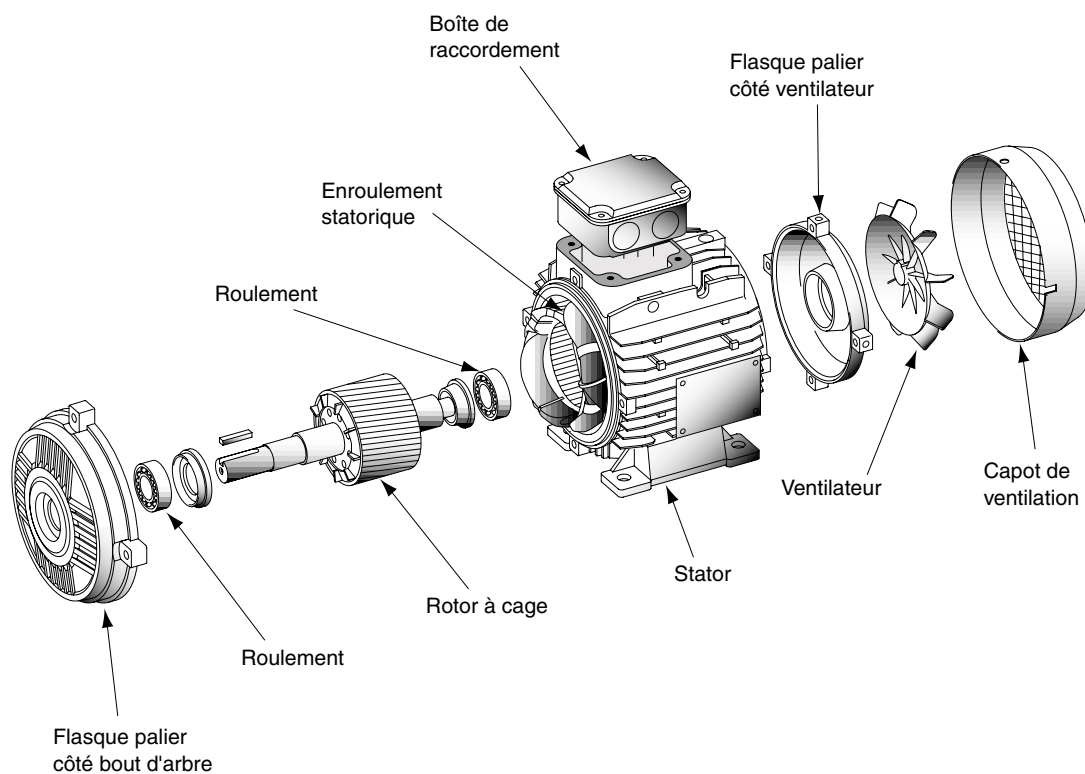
Eclaté d'un moteur à rotor à cage.
